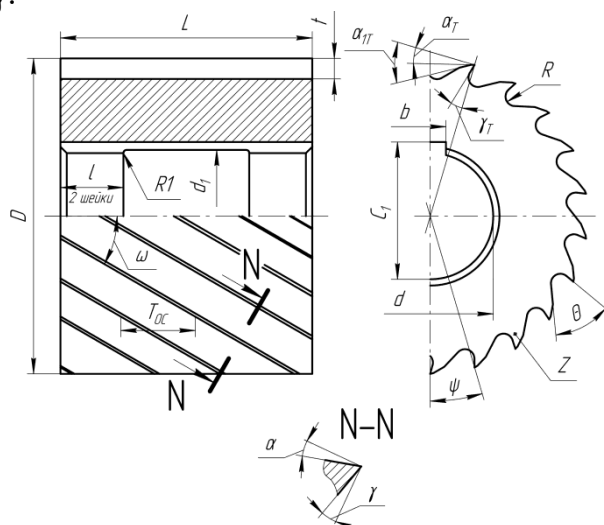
Конструктивные и геометрические параметры торцевых фрез
